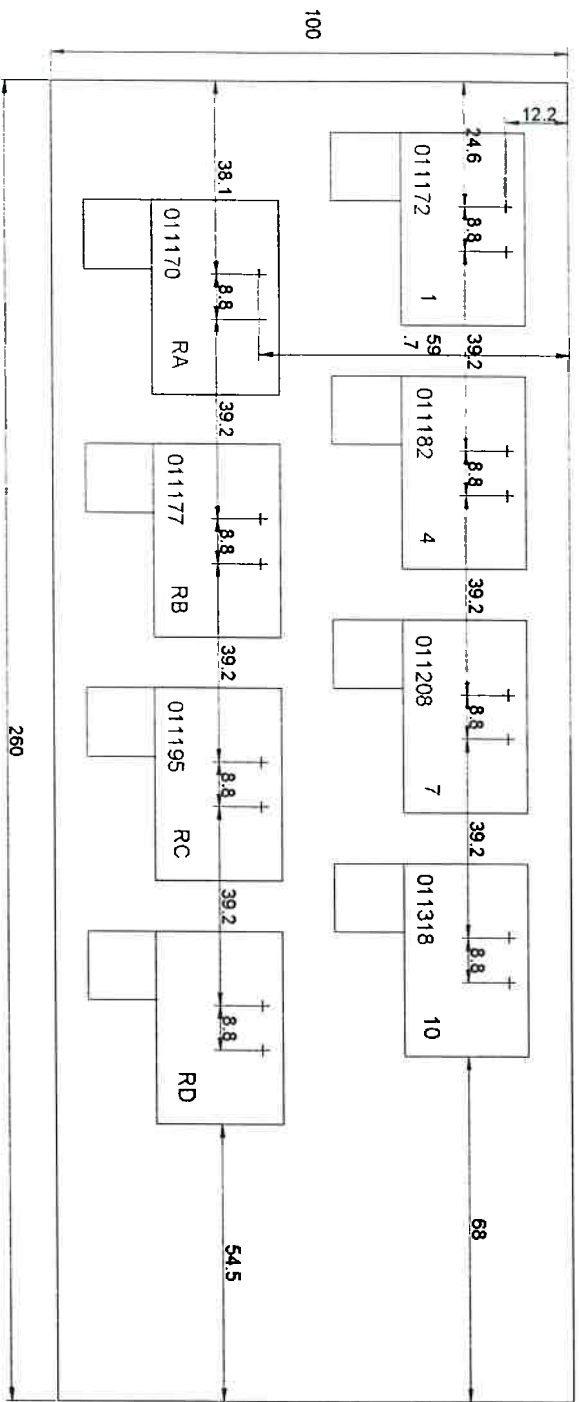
Desenho das disposição dos sensores de pressão na placa de circuito impresso. Cada sensor está identificado pelo seu número de série e pelo número do terminal de saída onde será conectado.
